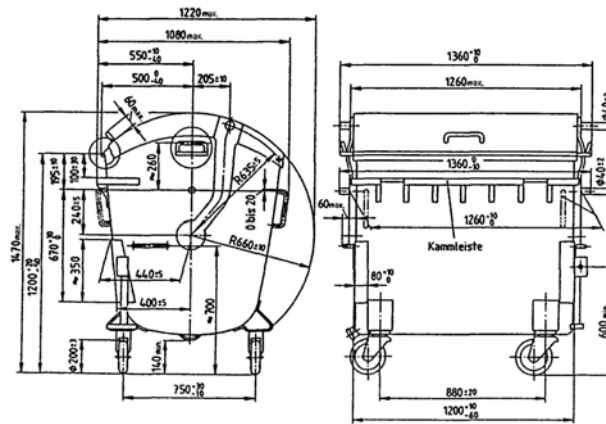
Grundkonstruktion MGB 500-1.100 Stahlblech mit Runddeckel
